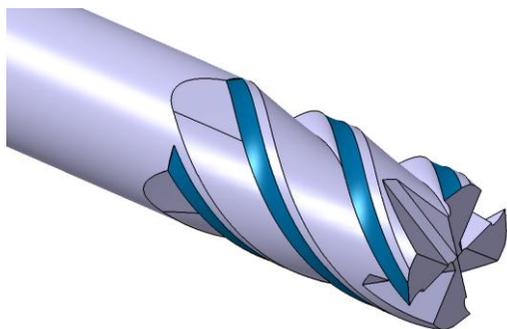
Заготовка, используемая для изготовления фрезы
